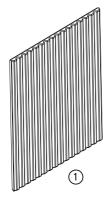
Revêtement de la chambre de combustion FINA F
